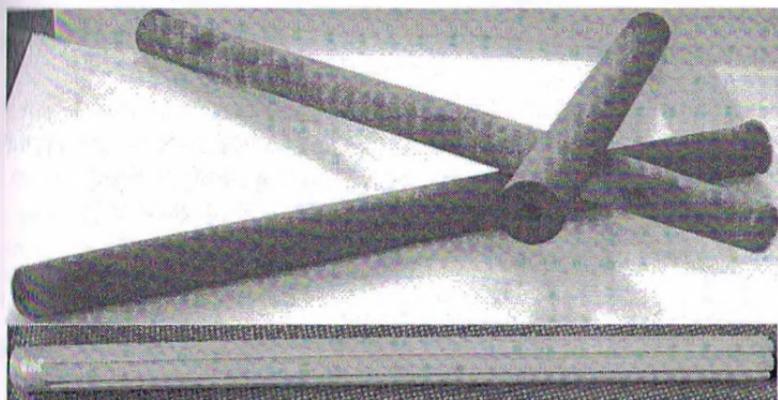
Вид прессовок с гладкой поверхностью и КПС со сформованными паровыми каналами
